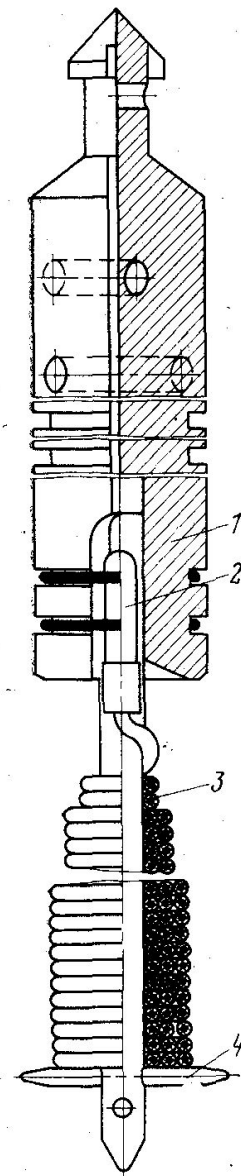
Торпеда корпусная из детонирующего шнура типа ТКДШ
